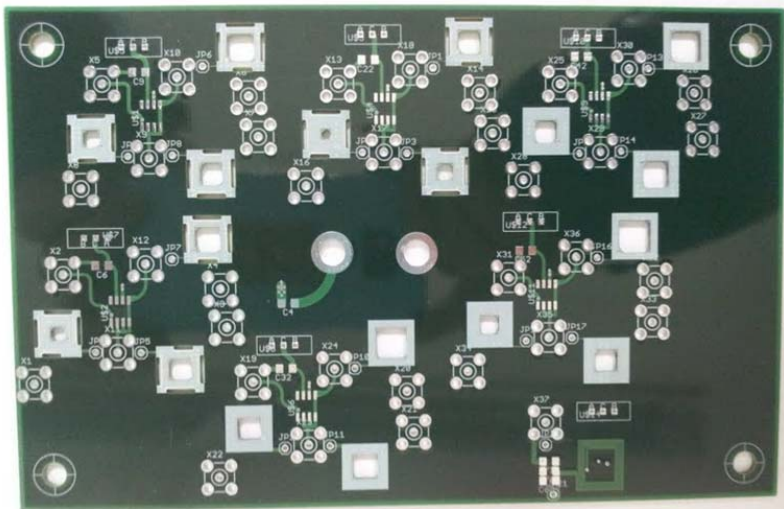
PCB 보드에 구현된 총 18가지의 인덕터들
